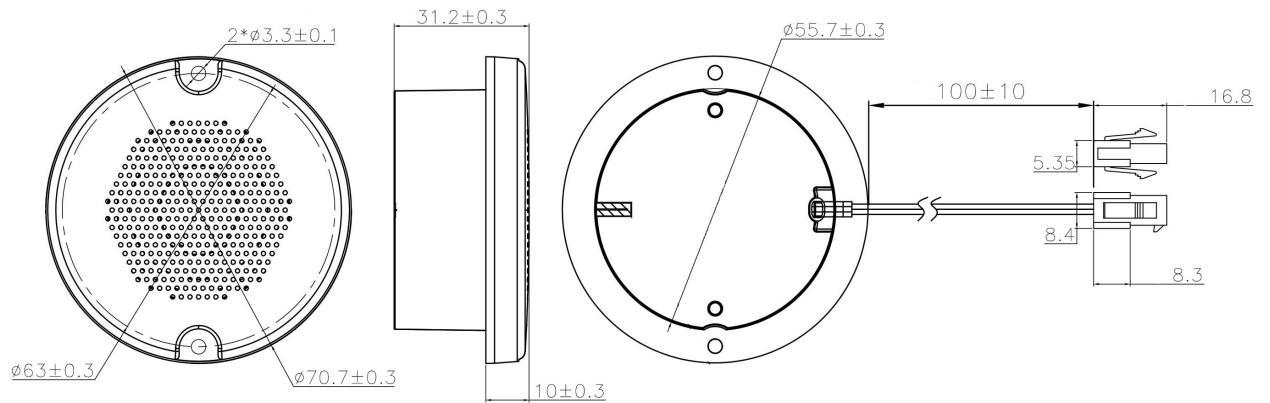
Габаритный чертёж Громкоговорителя ГМ-3
